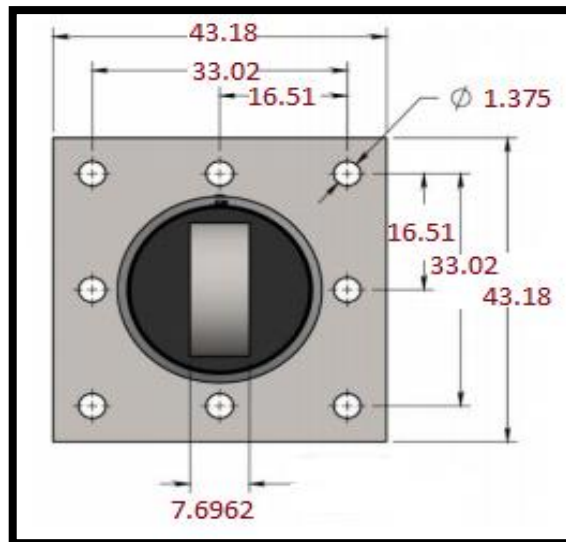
Dimensiones de la placa base para el disipador de 330 kip. Fuente: Propia.
